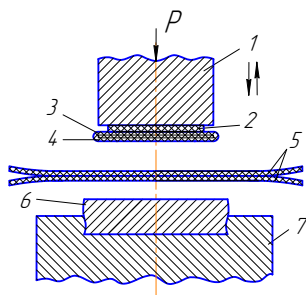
Схема термоимпульсной сварки:
